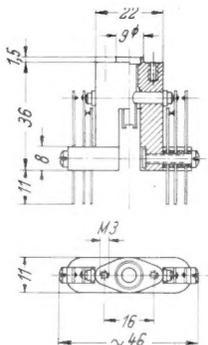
Die wichtigsten Abmessungen der Schaltbuchse
